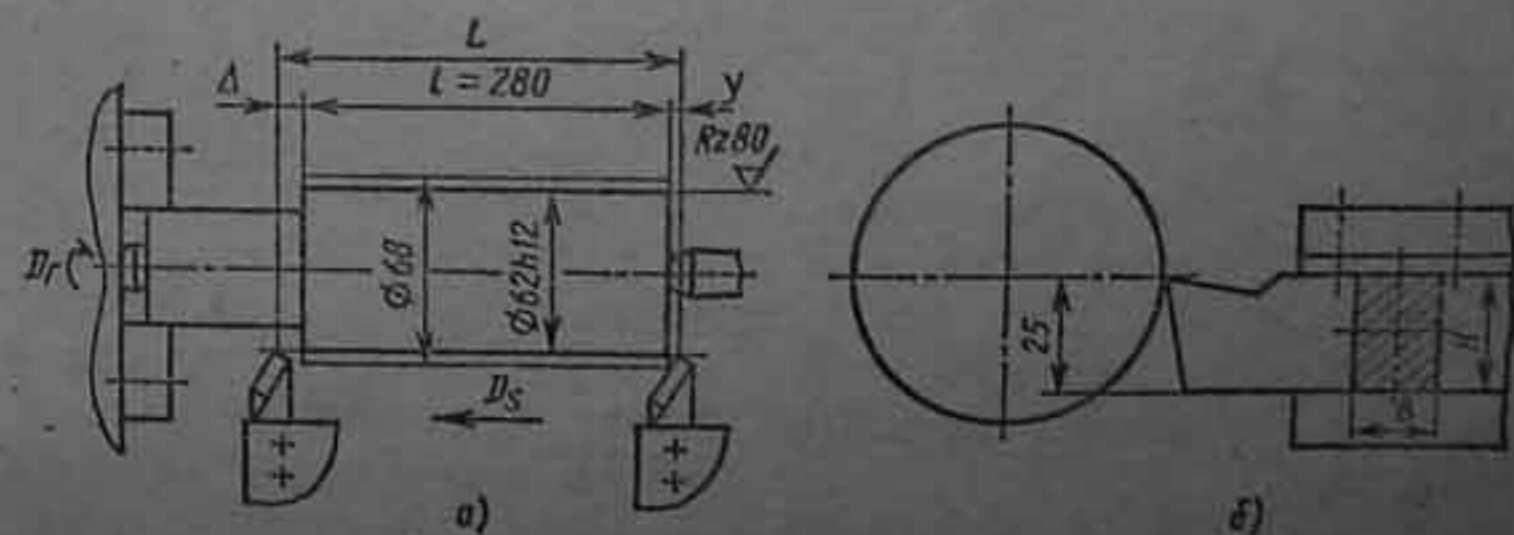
Эскизы обработки к примеру 17 (а) и установки резца (б)
